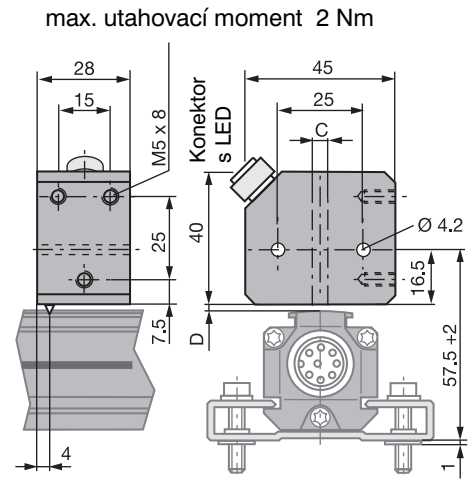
Rozměrový výkres (BTL5...P-S 32 odměřování s volným magnetem BTL5-P-3800-2)
